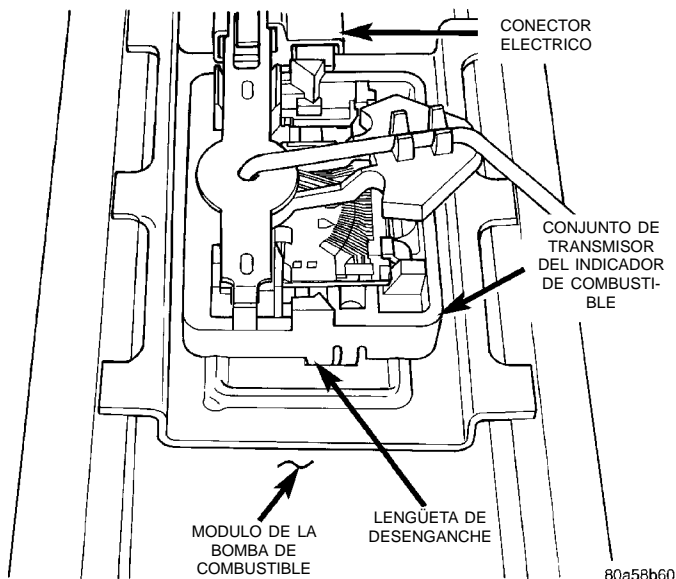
Lengüeta de desenganche del conjunto de transmisor del indicador de combustible
